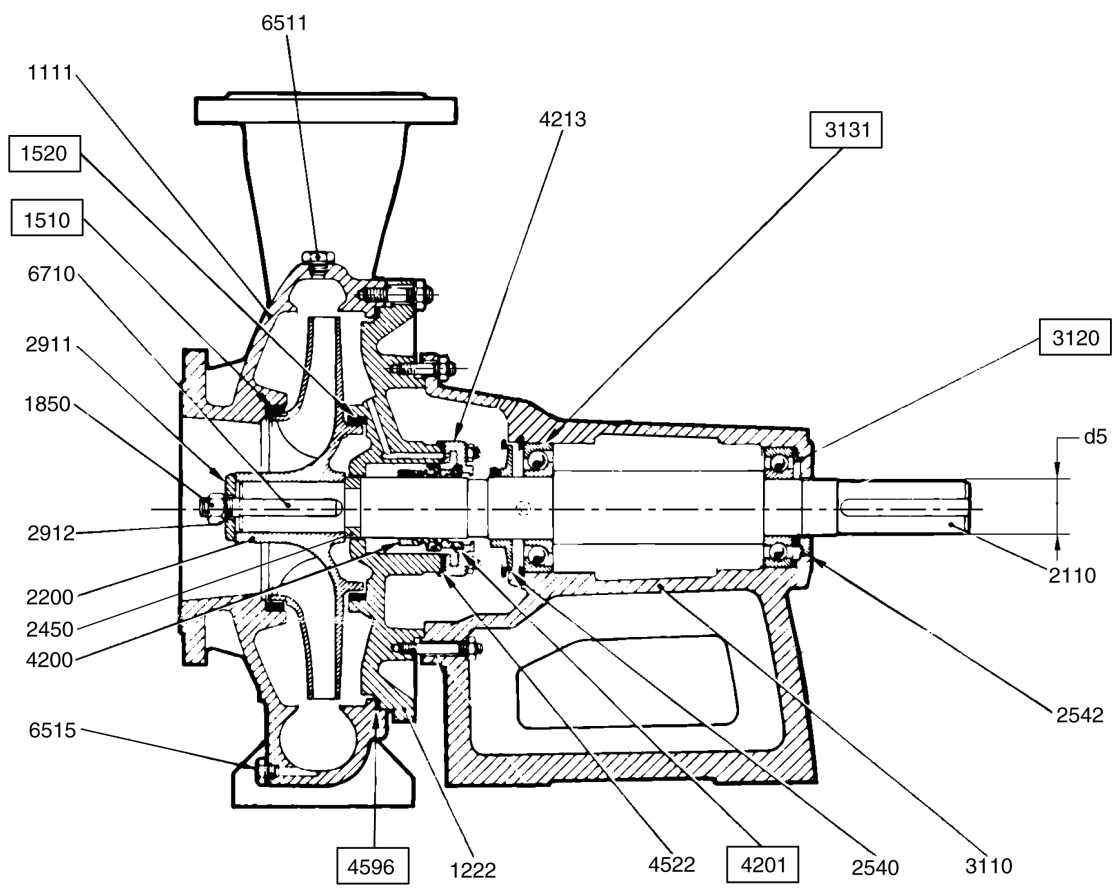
Plano seccionado, NK 250-310 "sobredimensionada"
